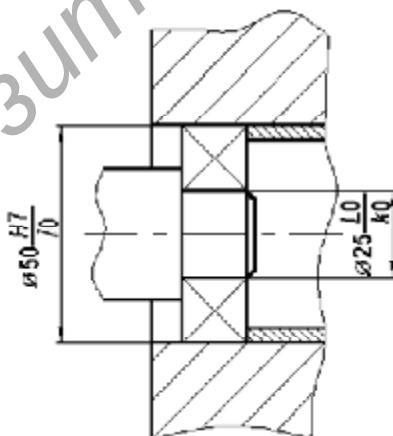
Обозначения посадок подшипника на вал и в отверстие корпуса
